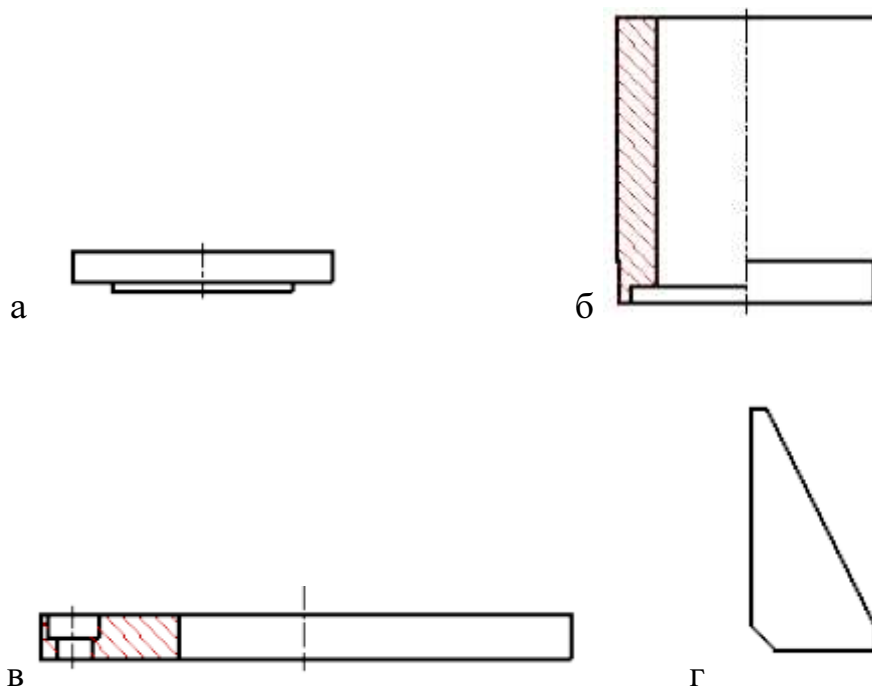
Эскизы деталей, входящих в сварную сборочную единицу:
